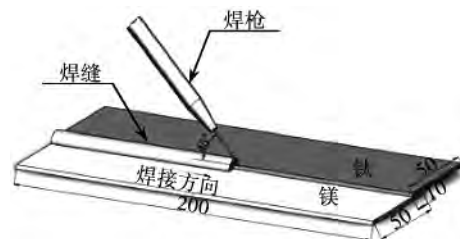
镁/钛异种金属 CMT 焊接示意图 (mm)
